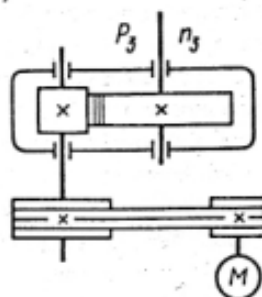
Исходная схема цилиндрической прямозубой передачи
